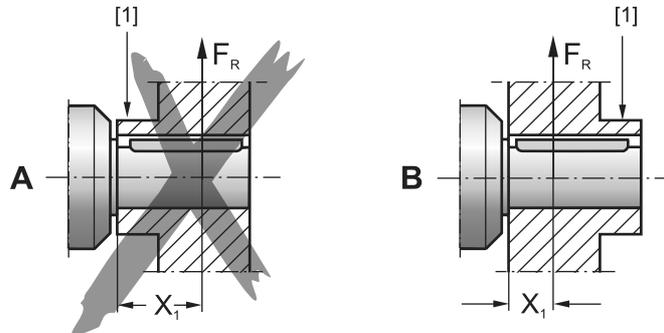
disposizione di montaggio di una ruota dentata o di un rocchetto per catena 06700AXX
